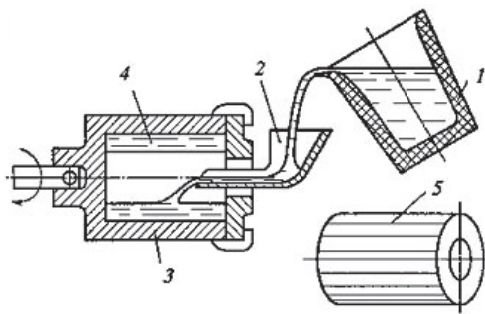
Схема устройства горизонтальной машины для центробежного литья: 1 – ковш с жидким металлом; 2 – желоб; 3 – форма, вращающаяся вокруг горизонтальной оси; 4 – затвердевающая полая отливка; 5 – готовая отливка
